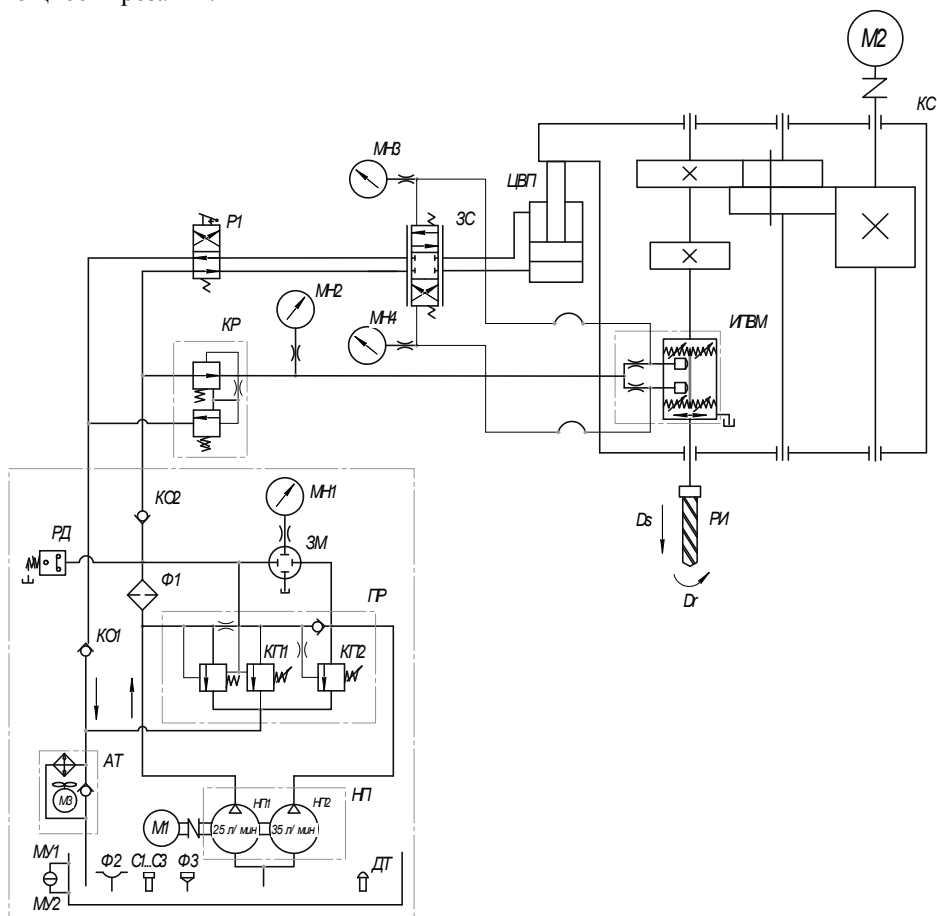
Комбинированная схема приводов главного движения и вертикальной подачи станка ЛФ260МФ1 с системой адаптивного управления:
